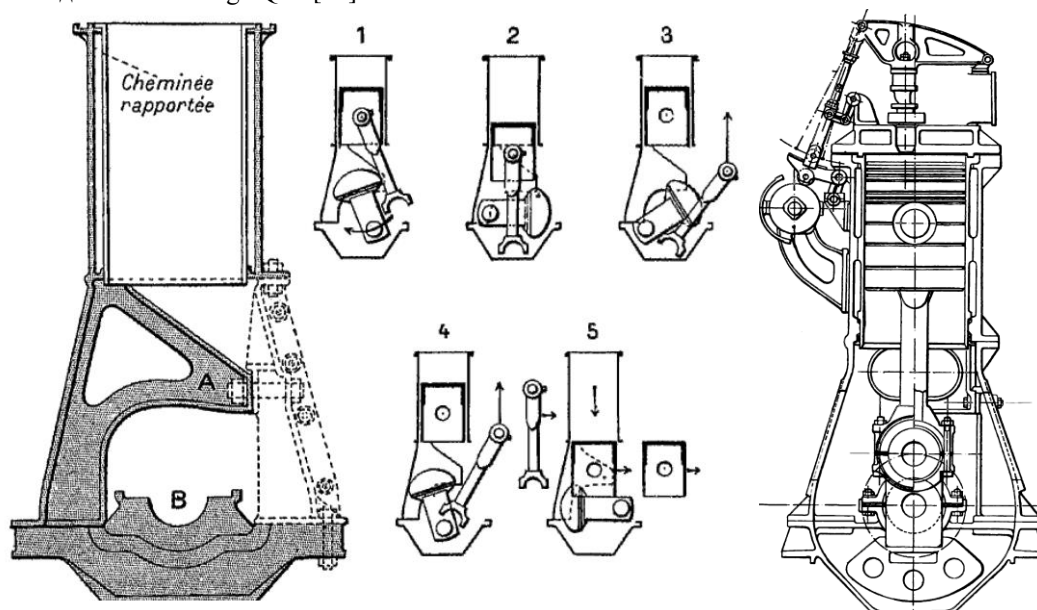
Конструкция картера двигателя со съемной боковой стойкой, позволяющая осуществлять выемку поршней без снятия крышек цилиндров, и поперечный разрез двигателя
